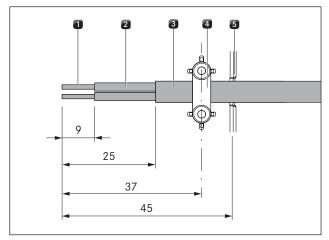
Abisolierlängen und Montageposition der Anschlussleitung
